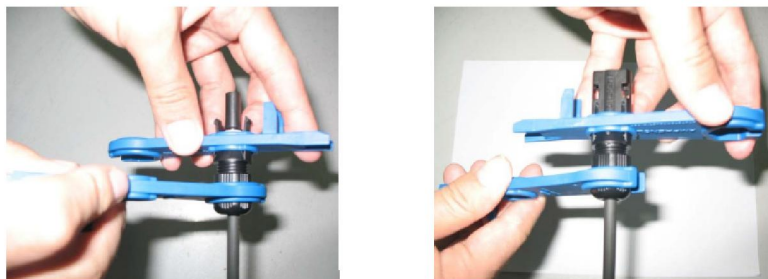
Гаечный ключь2,6 ~ 2,9 НМ
